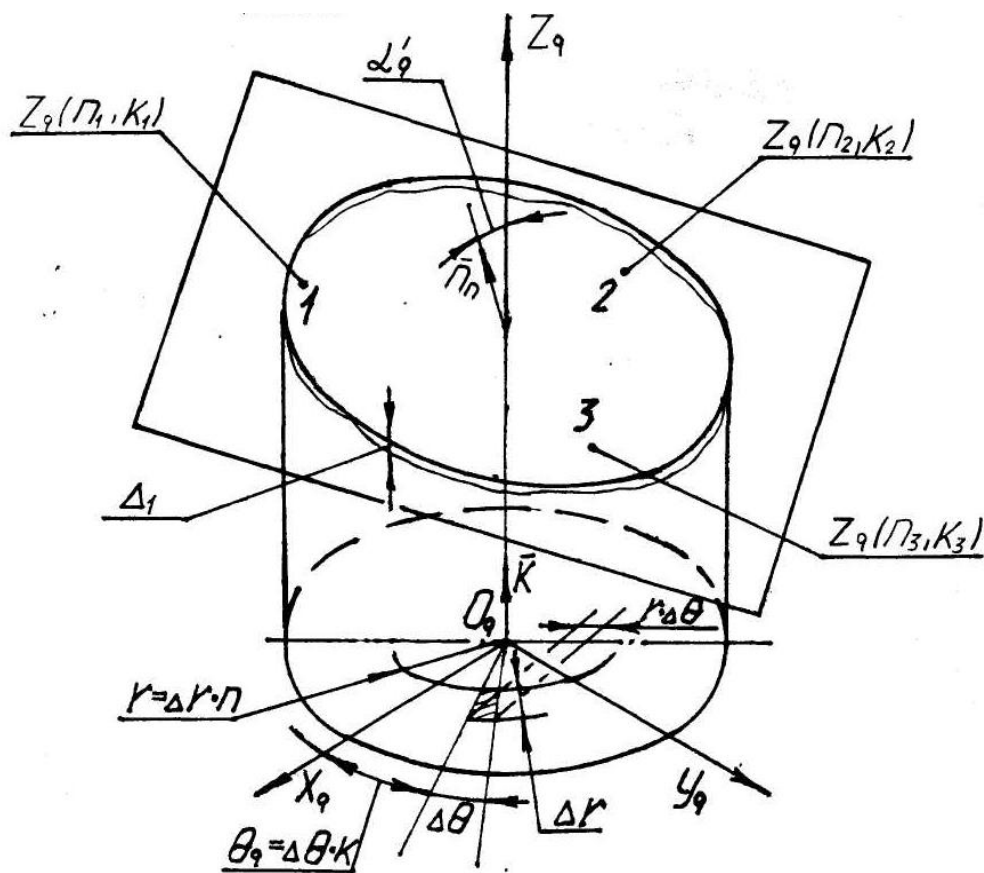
Схема определения геометрической погрешности формообразования торца цилиндрической детали
